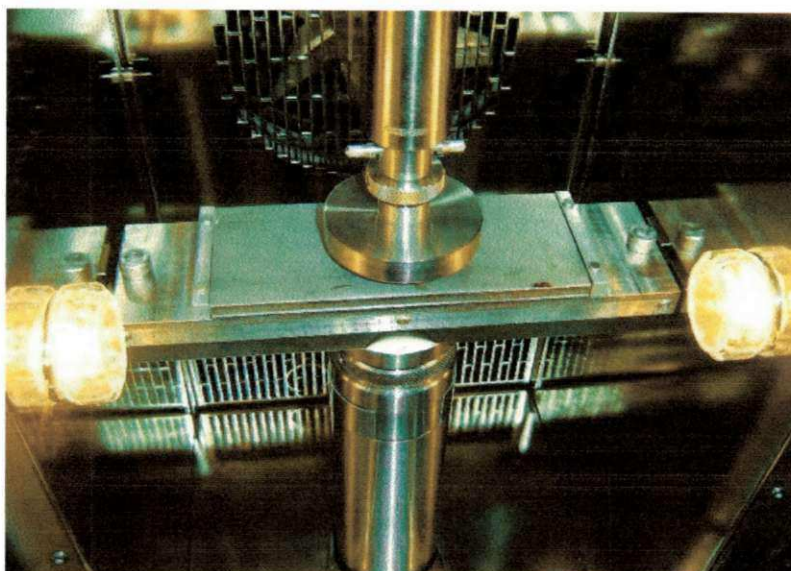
Sistema de moldagem por pressão adaptado na máquina Instron 5582.
